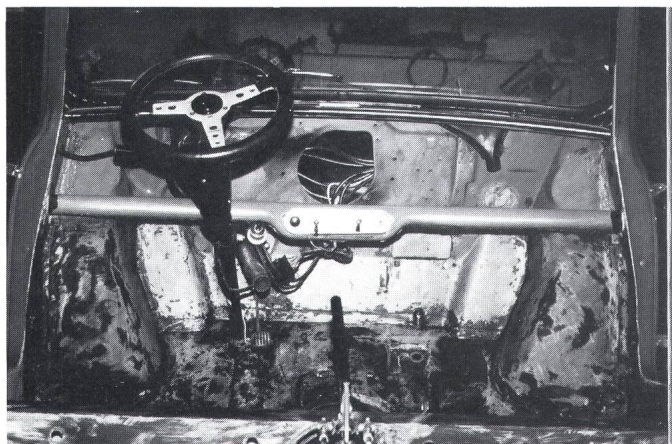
So sah das Fahrzeug nach der kompletten Demontage der Innenausbauten aus
